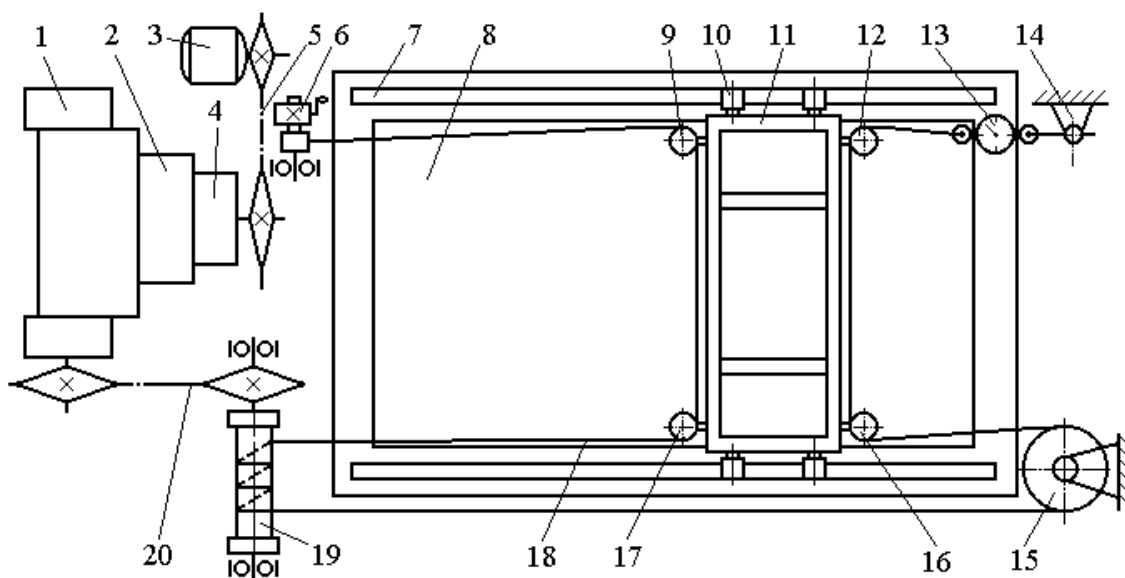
Кінематична схема приводу динамометричного візка:
